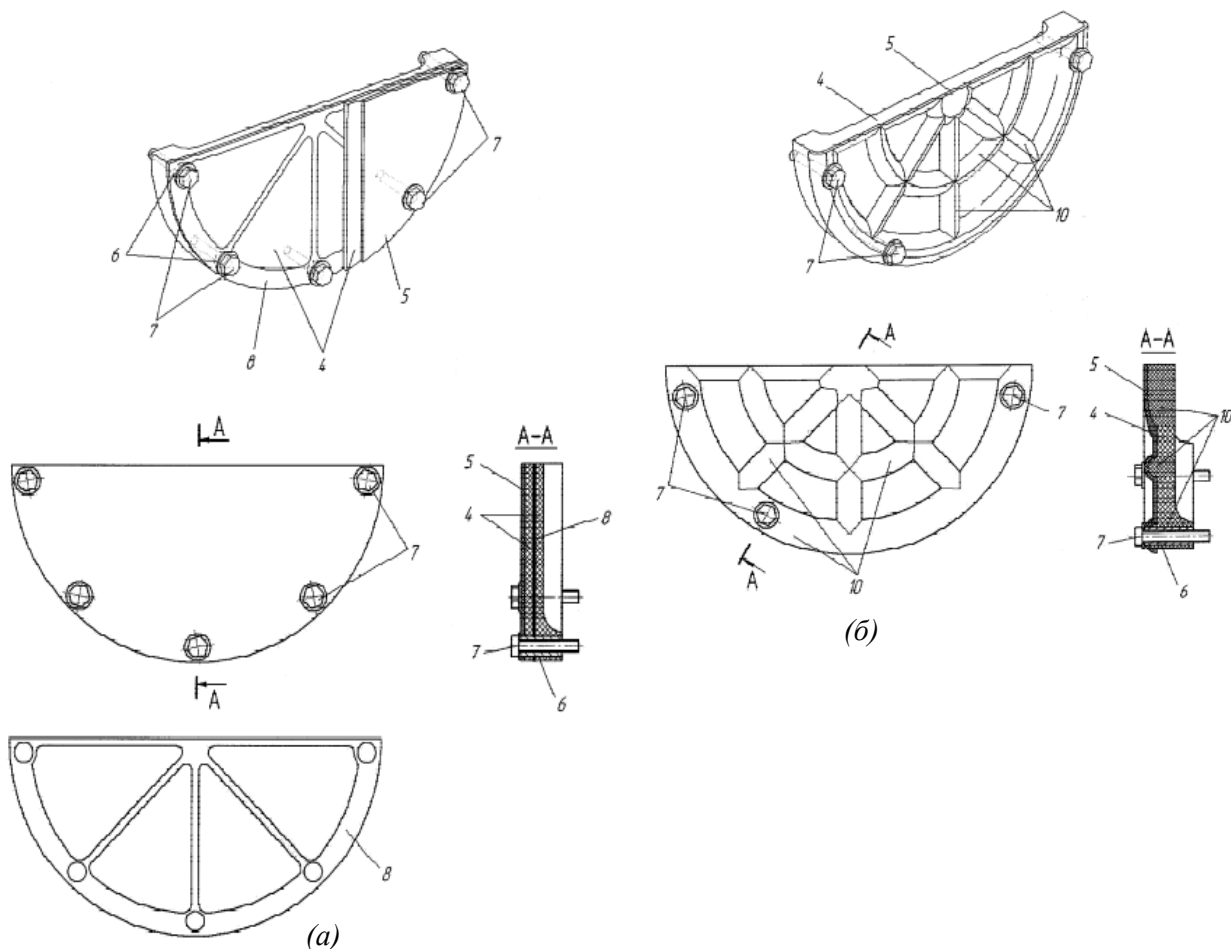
Различные варианты конструктивного исполнения кожуха картера сцепления силового агрегата (а, б):
